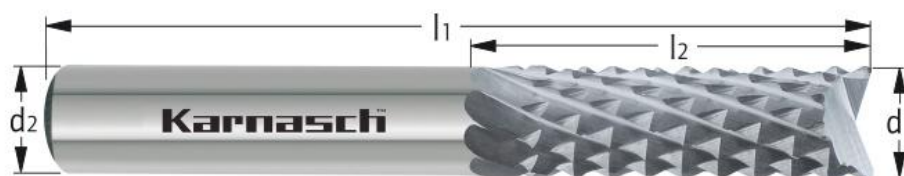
Фреза роутерного типа для черновой обработки кромок
